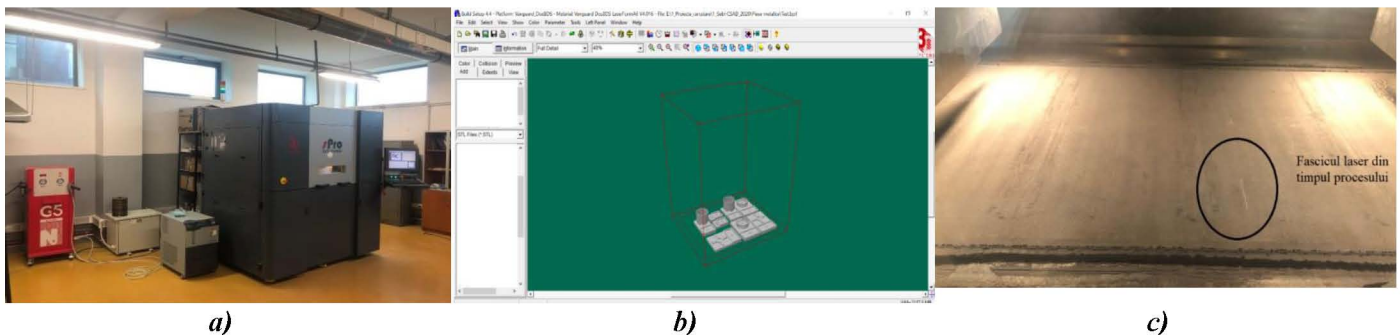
Fabricarea aditivă a componentelor motorului electric utilizând procedeul SLS: a) instalația 3D System SPRO 60 SD; b) pregătirea pentru fabricare a componentelor motorului electric; c) inițierea procesului de fabricare a pieselor
